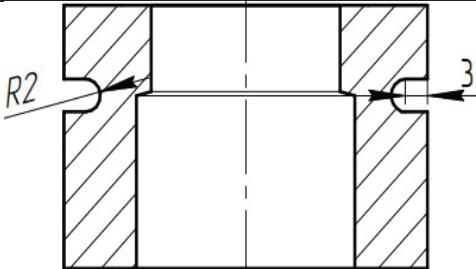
Послідовність оброблення поверхонь деталі «Корпус форсунки»
